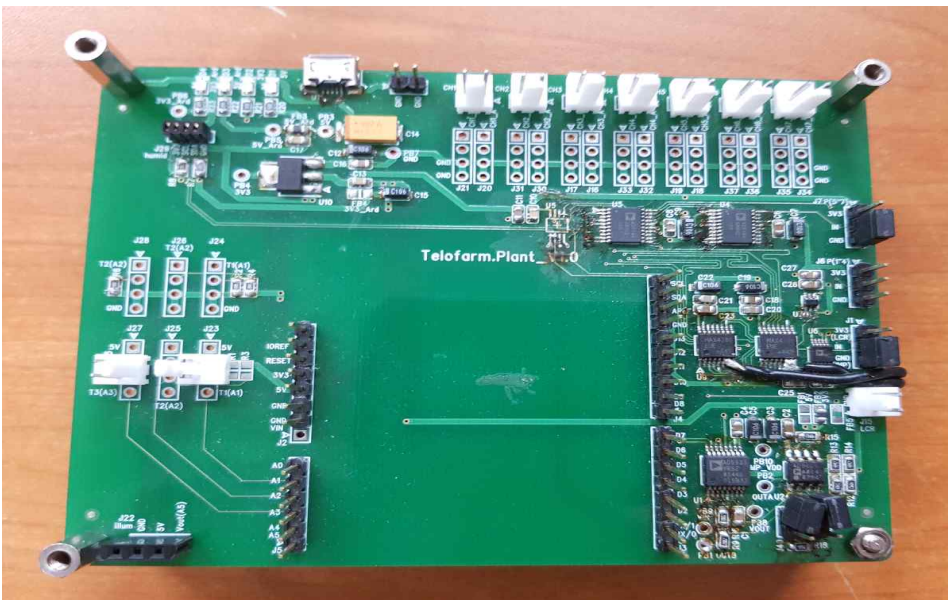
개발한 전자 장치의 PCB 조립 사진
